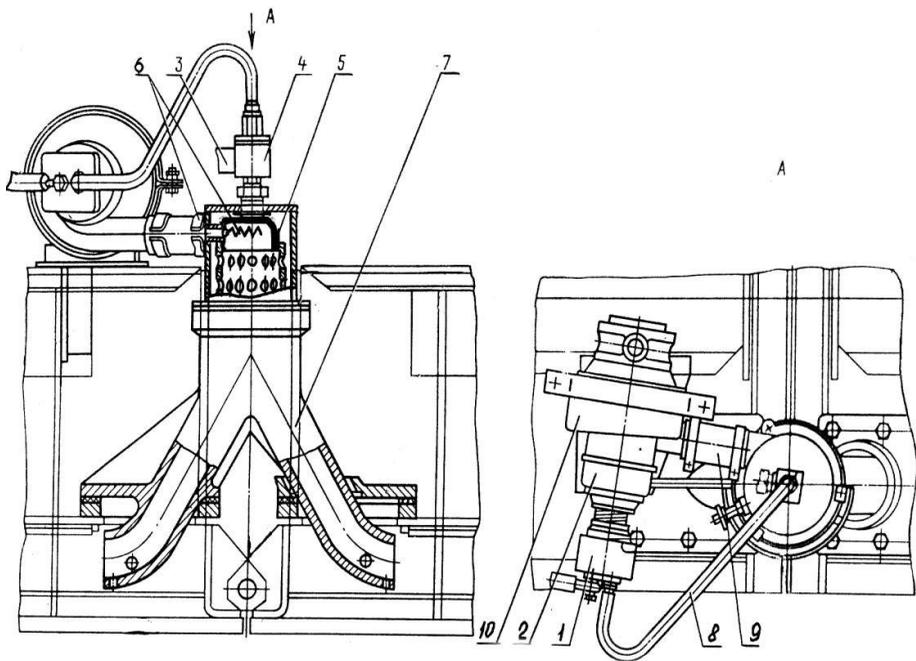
Газовый механизм обогрева выглаживающей плиты:
